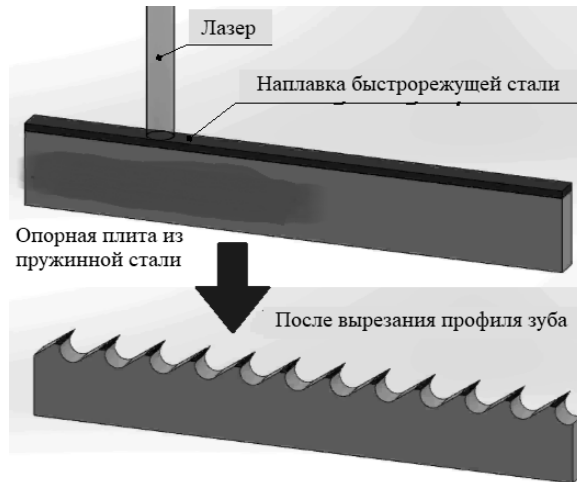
Производство биметаллического режущего инструмента с использованием технологии лазерной сварки
